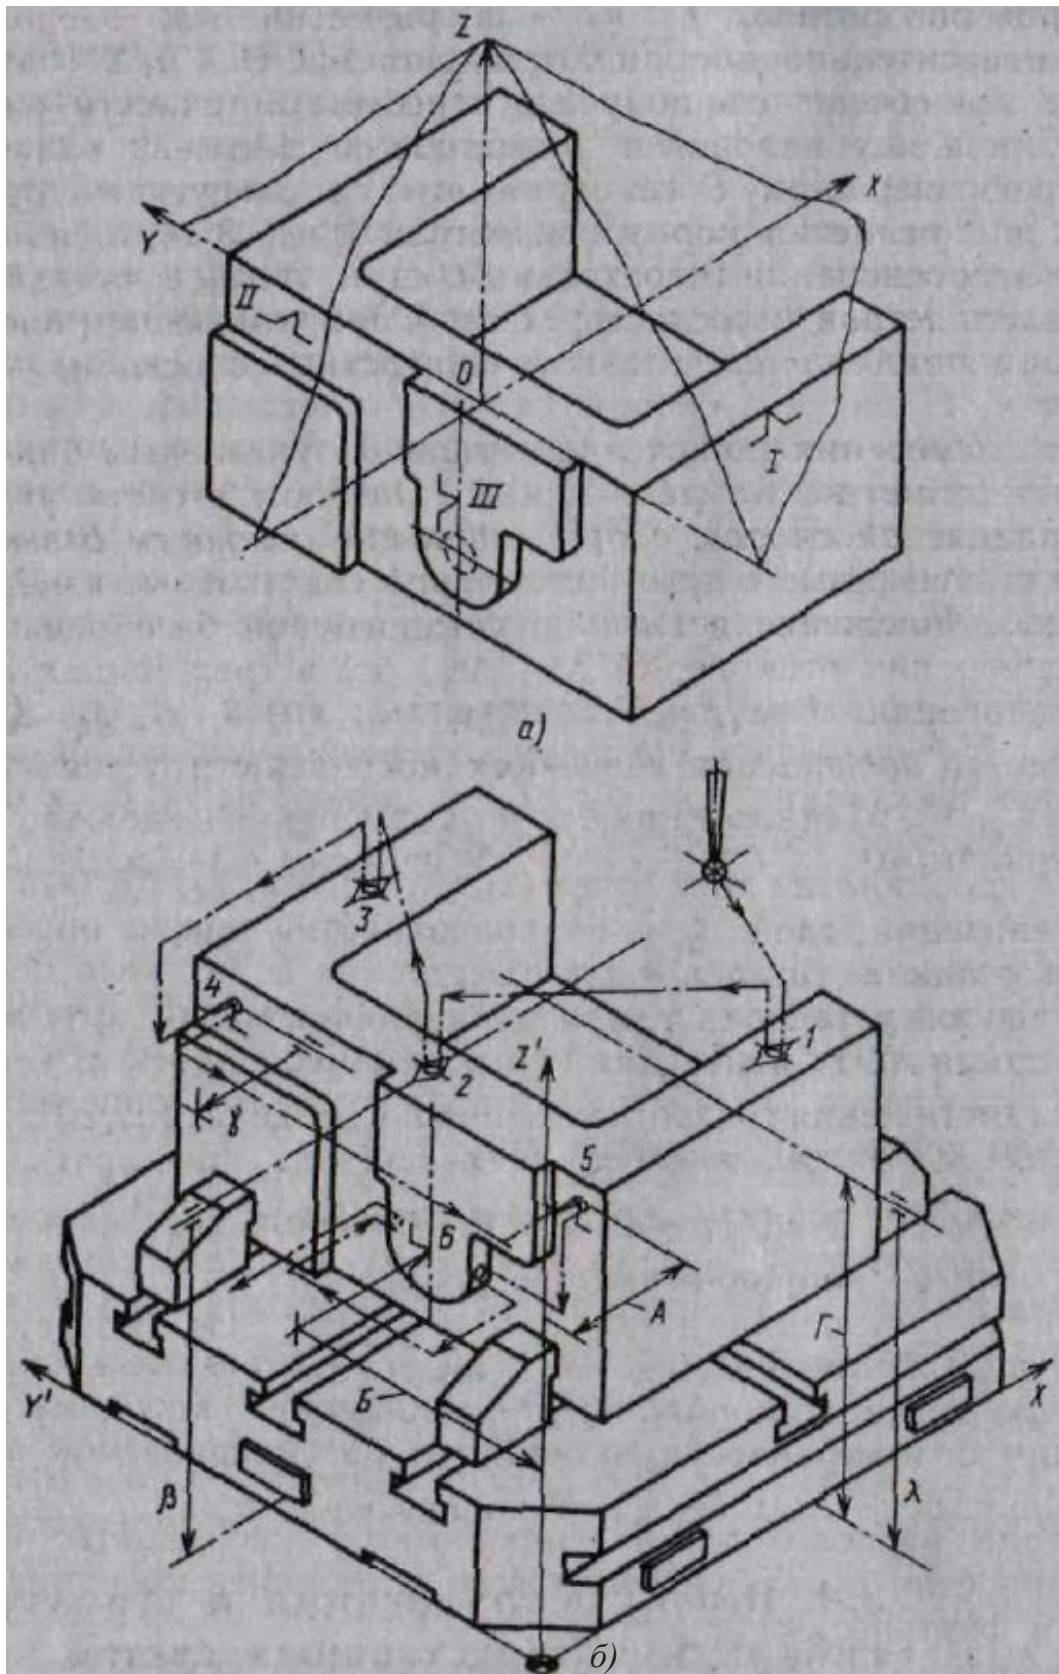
Установка заготовки на спутнике по разметке с применением координатно-измерительной машины: а – координатная система баз заготовки; б – измерение положения заготовки при ее установке
